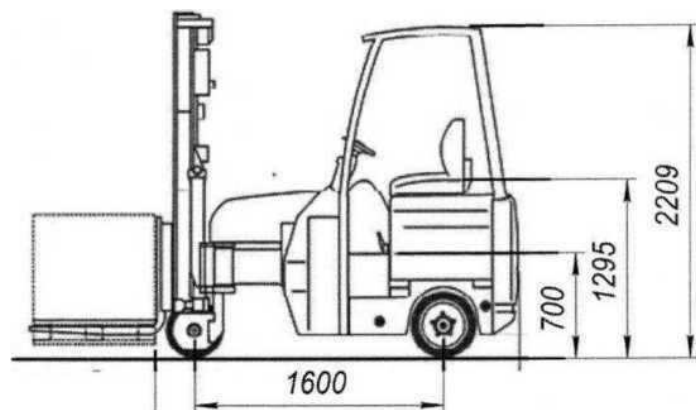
Общий вид узкопроходного погрузчика Bendi B45SE с габаритными размерами
